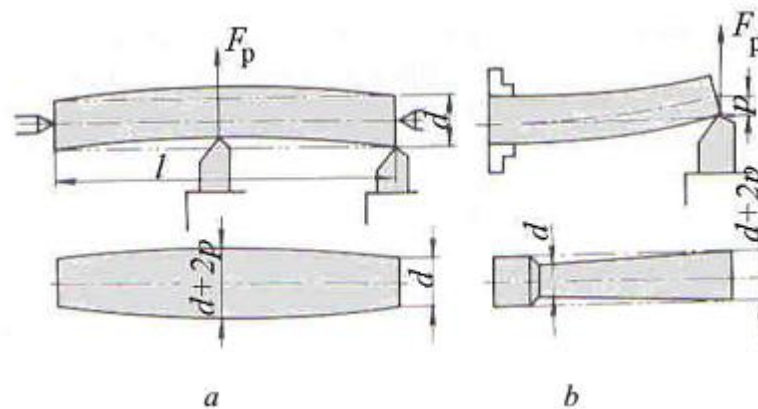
výsledná tvar obrobku, soustruženého při upnutí ve sklíčidle [2]
